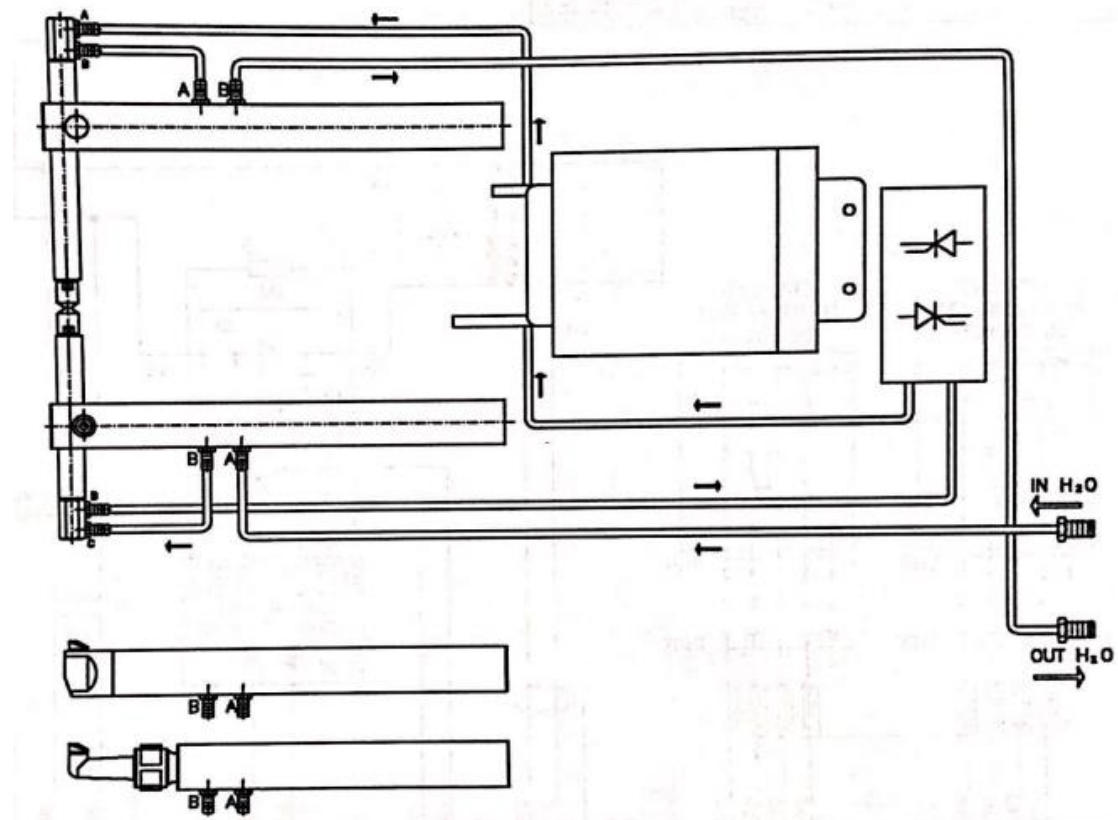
Esquema de Enfriamiento de la Soldadora de Punta.
